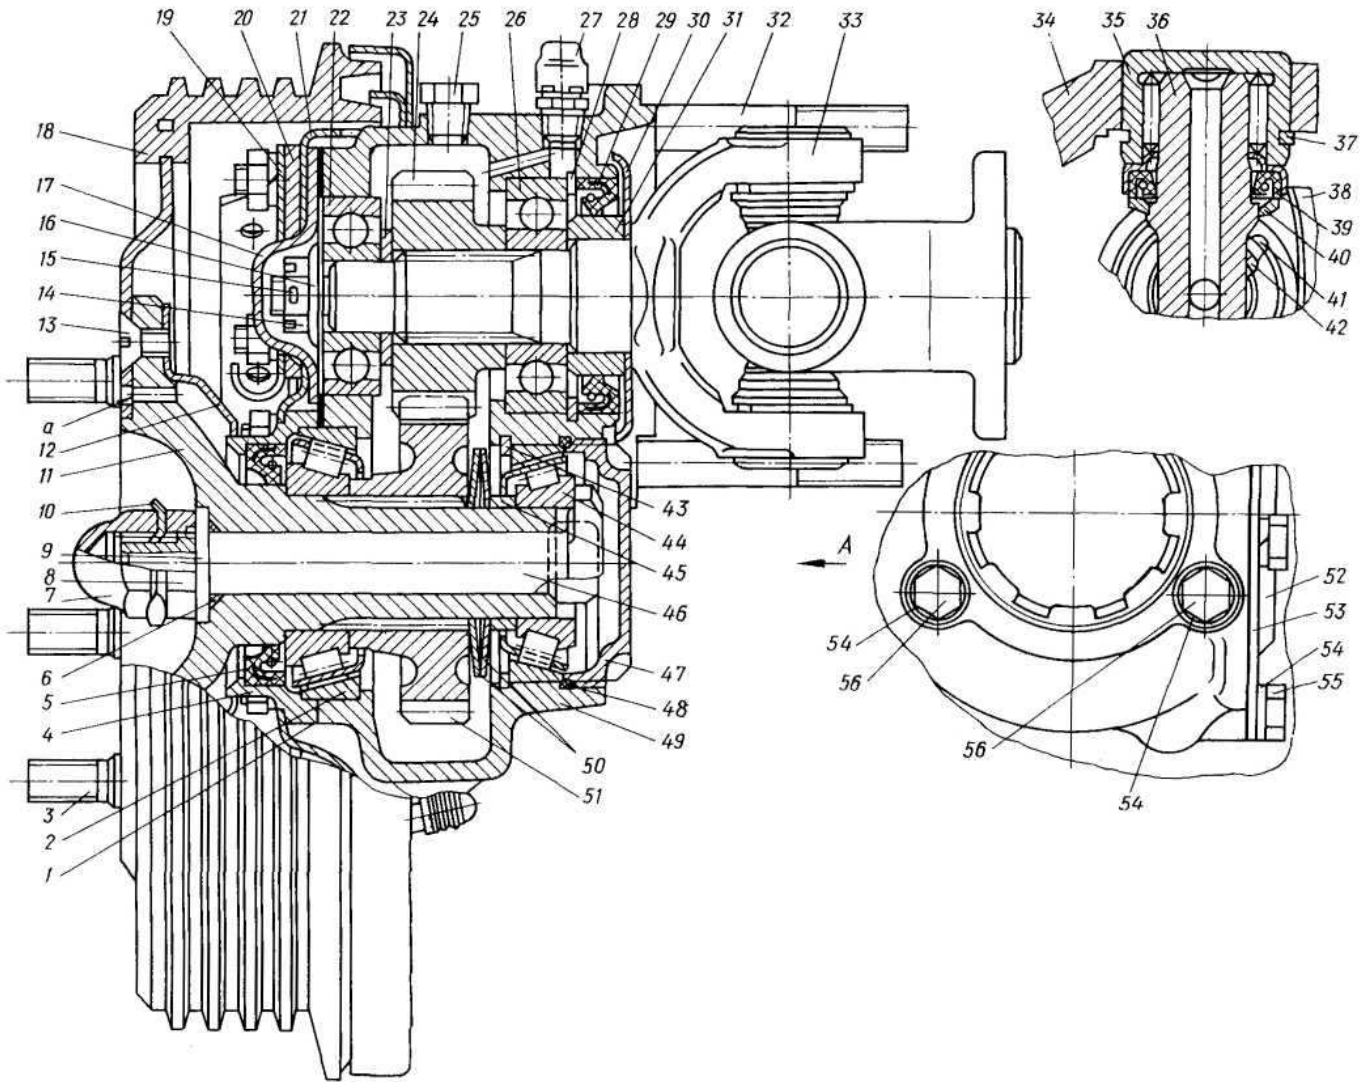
Редуктор колёсный (с тормозом в сборе):
